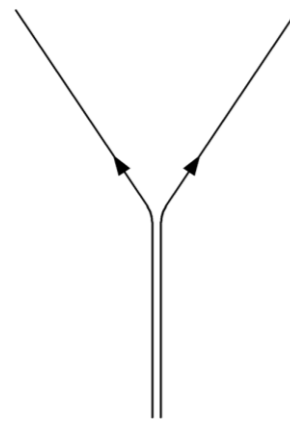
Schweißpfadführung - Lage 2
